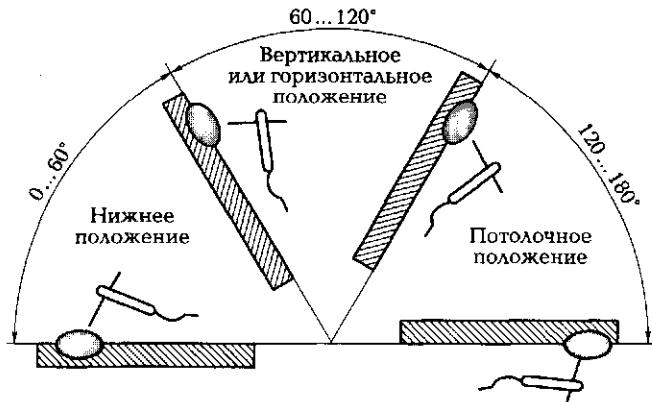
Основные пространственные положения сварных швов
